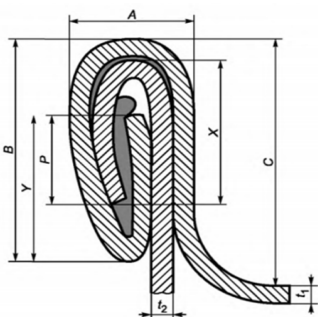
Профиль закаточного шва (A – толщина шва, мм; B – высота шва, мм; C – глубина посадки донышка или крышки, мм; P – перекрытие шва, % (определяют по формуле 1); x – длина крючка корпуса, мм; y – длина крючка донышка или крышки, мм; t_1 – толщина донышка или крышки, мм; t_2 – толщина корпуса, мм)
